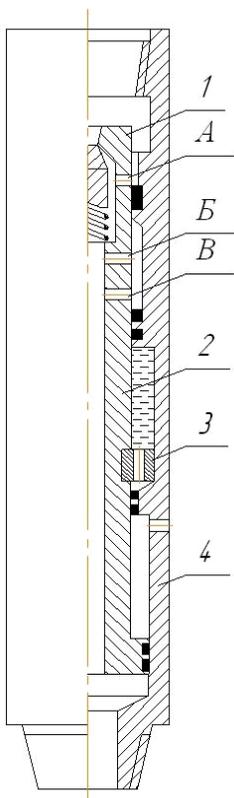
Схема гидравлического штуцера: 1 – обратный клапан; 2 – подвижный шток; 3 – поршень тормозной камеры; 4 – корпус
